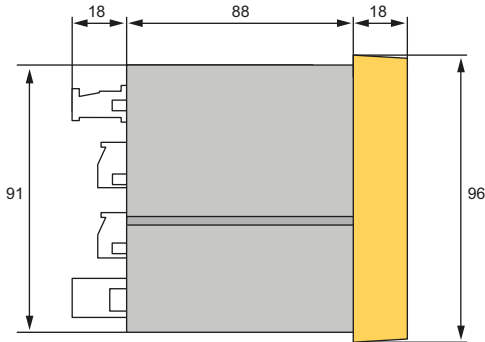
Maßbild PEM533 (Seitenansicht)
